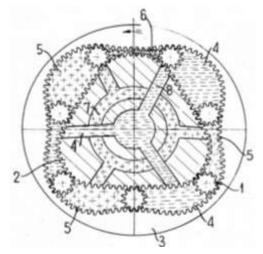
Конструкция гидромотора, разработанного Bohdan Sieniawski: 1 — сателлит; 2 — внутренний кулачок; 3 — внешний кулачок; 4, 7, 8 — каналы для подачи жидкости; 5, 6 — рабочая жидкость
